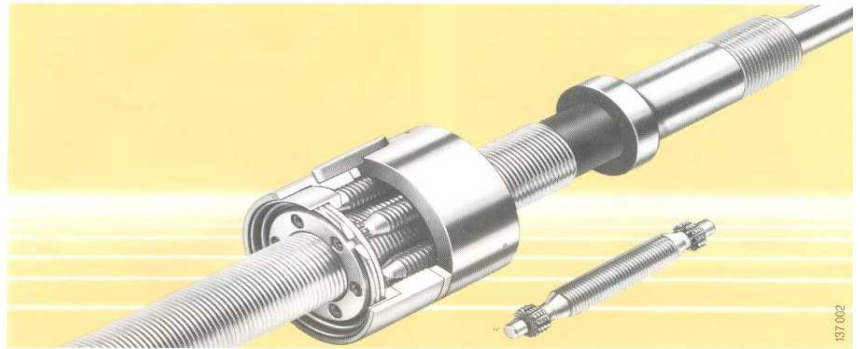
INA-Rollengewindetrieb mit geteilter Gewindemutter
